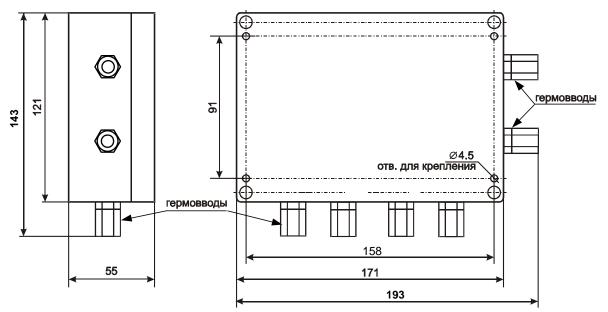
Габаритные и присоединительные размеры КД2 ІР65
